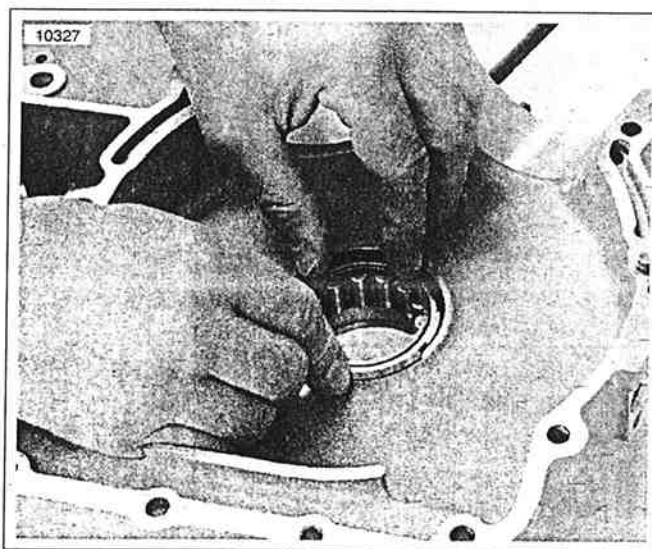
Instalación del anillo de retención del cojinete izquierdo principal
